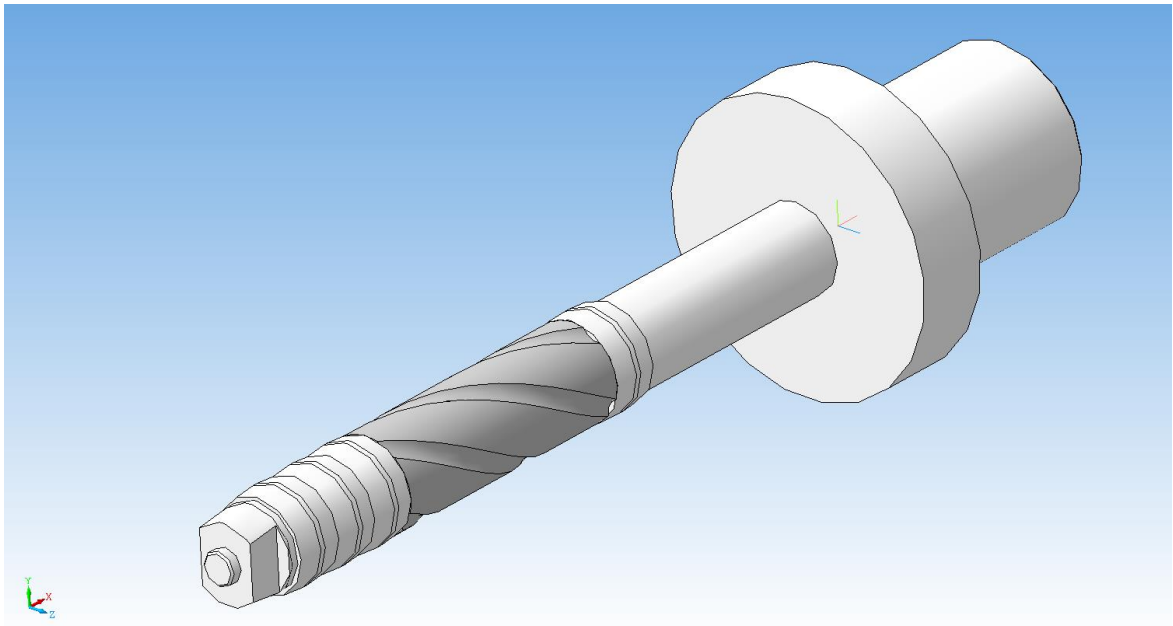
Загальний вигляд деформуючої прошивки
